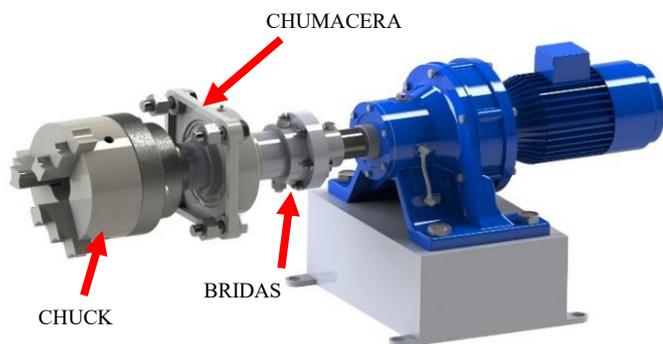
Eje principal de la mesa de soldadura. Compuesto principalmente por un Chuck de 3 mordazas soportado a una chumacera de pared UCF 216, unido a una flecha junto con el eje de un motorreductor trifásico de 1 HP.
